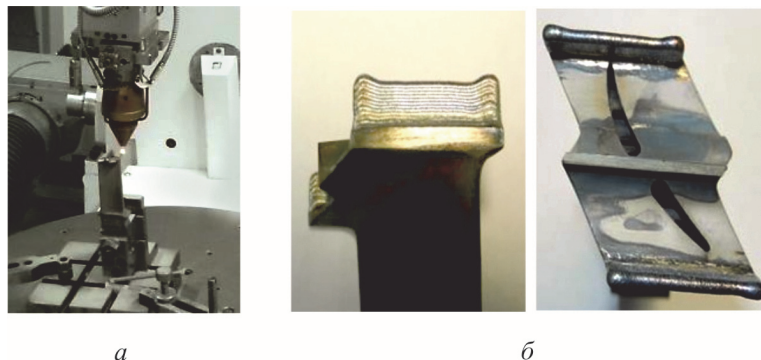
Процесс лазерной газопорошковой наплавки (а) и внешний вид восстановленных крайних гребешков бандажных полок рабочих лопаток ТВД (б)
